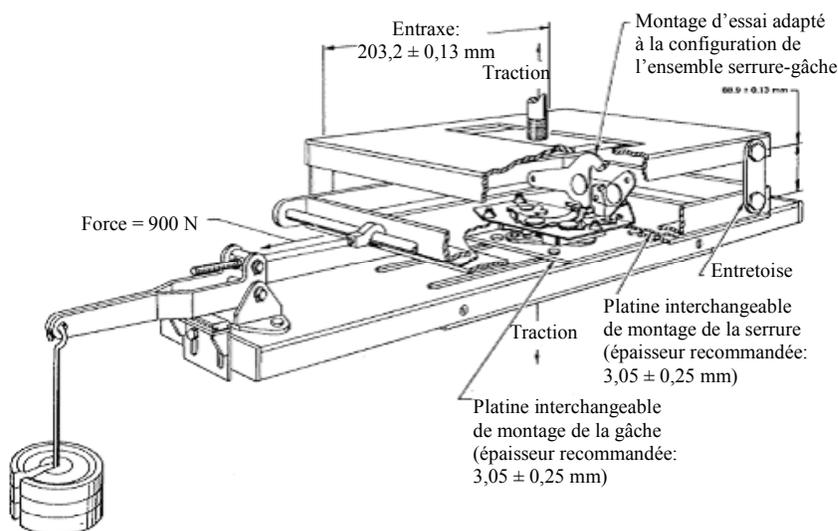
Serrure de porte – Montage pour essai n° 1 d'application d'une force de traction
